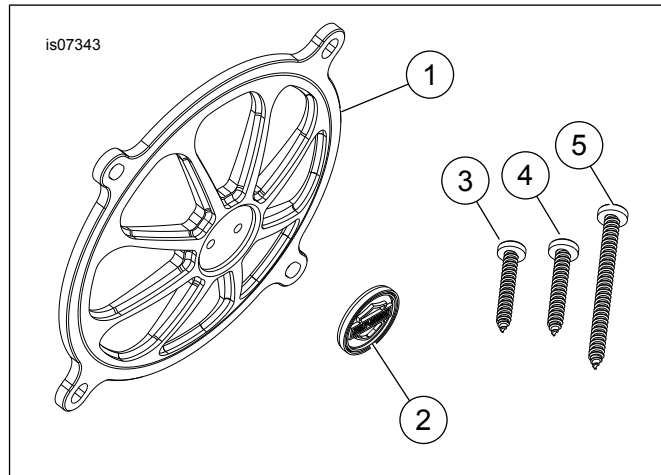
Pièces de rechange : Grille de haut-parleur Collection Burst
